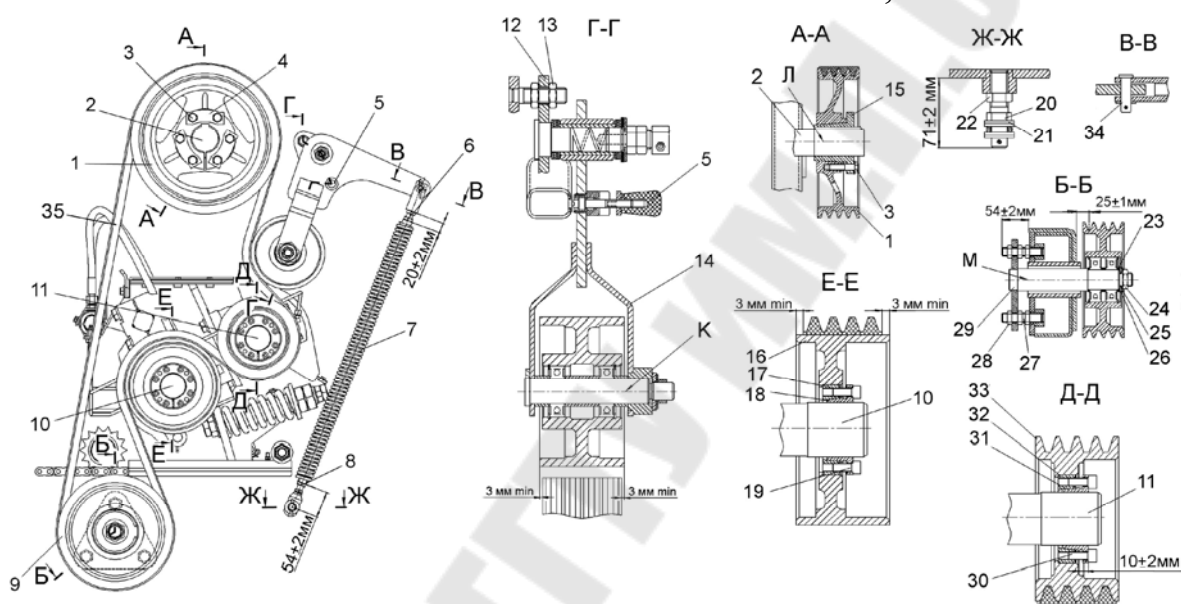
Схема регулировки привода доизмельчающего устройства: 1, 33 – шкивы; 2 – вал ускорителя; 3 – болт; 4 – пластина; 5 – фиксатор; 6, 8, 13, 22, 28 – гайки; 7 – пружина; 9, 16 – ролики; 10 – вал вальца нижнего; 11 – вал вальца верхнего; 12, 29 – опоры; 14 – рычаг; 15, 18, 31 – ступицы; 17, 23, 32 – втулки; 19, 30 – винты; 20, 34 – пальцы; 21, 26 – шайбы; 24 – гайка специальная; 25 – шайба специальная; 27 – шпилька; 35 – ремень; К – ось рычага; Л – ось вала ускорителя; М – ось опоры
